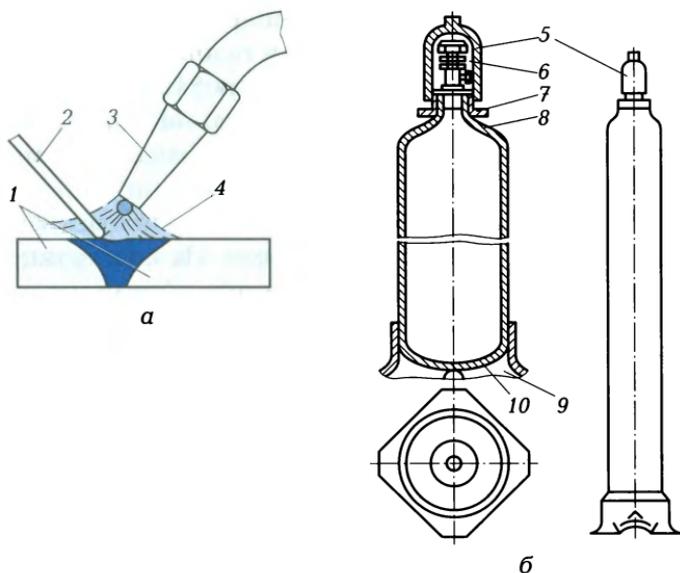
Схемы процесса газовой сварки (а) и кислородного баллона (б):
